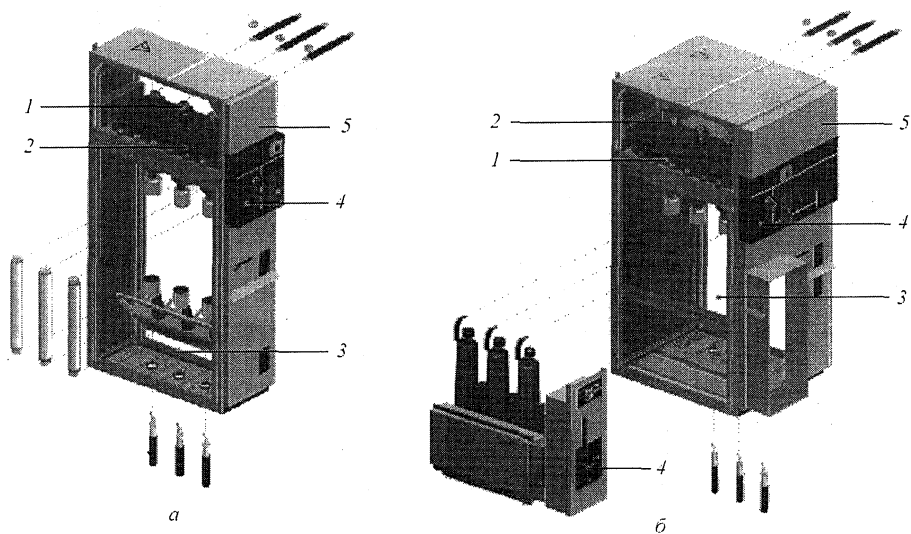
Конструкция ячейки: *а* — с выключателем нагрузки и плавким предохранителем; *б* — с выключателем; 1 — отсек трехпозиционного разъединителя (выключателя нагрузки) и заземляющего разъединителя в одном корпусе; 2 — отсек сборных шин; 3 — кабельный отсек и отсек выключателя; 4 — отсек привода; 5 — отсек релейной защиты и цепей вторичной коммутации
